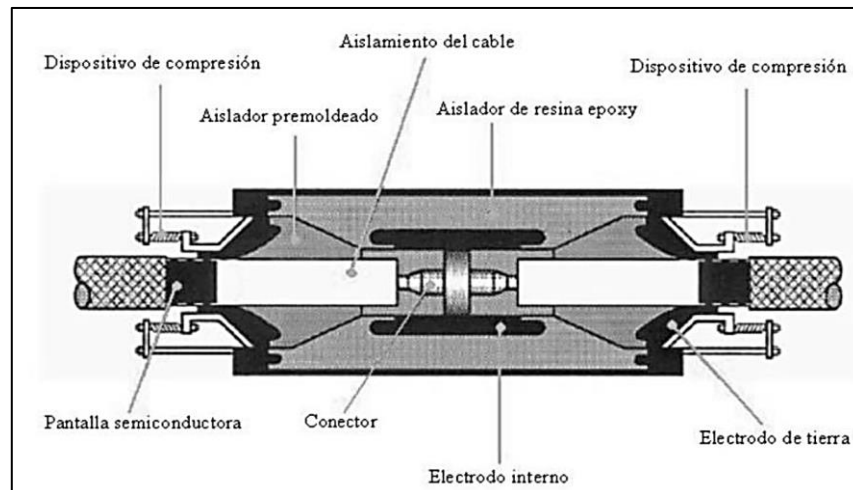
18 *Empalme premoldeado de tres piezas - partes.
